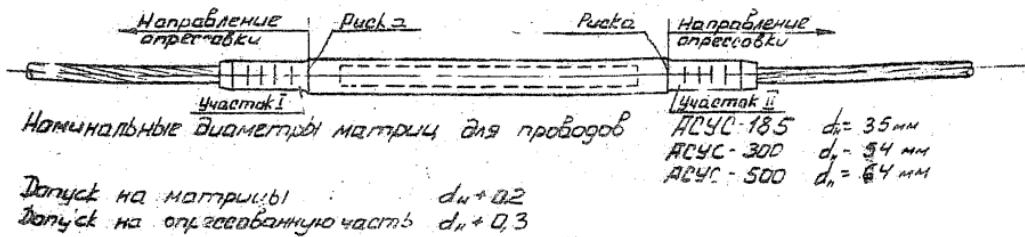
Опрессовка корпуса соединительного зажима САСУС
